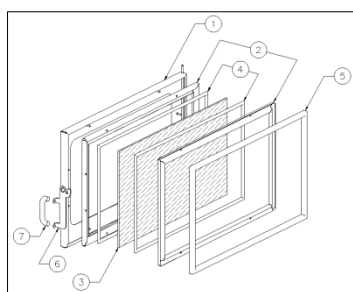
Vue explosée de l'assemblage de la porte
